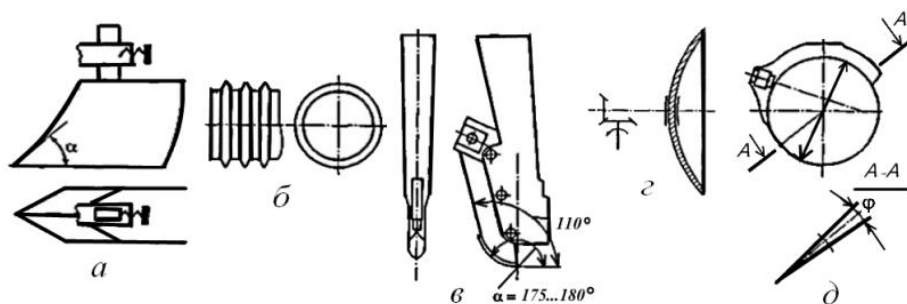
Типы сошников сеялок: а – коробчатый; б – бороздообразующий каток; в – анкерный; г – однодисковый; д – двухдисковый
